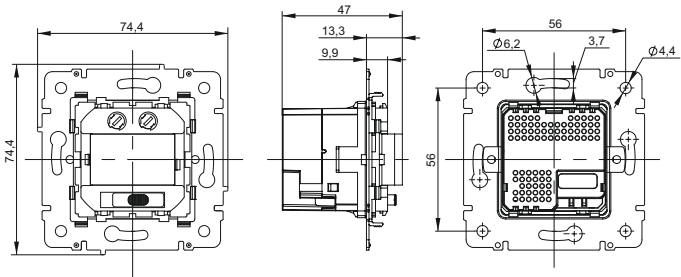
Габаритные и установочные размеры / Figure 1 – Overall and installation dimensions / 1-сურет – Габариттік және орнату өлшемдері / Figura 1 – Dimensiunile generale și de instalare / Şekil 1 – Ümumi və quraşdırma ölçüləri / სკაჲ 1 – ღსუჲასიოჲ Ⴁ სთეოაჲრმას ჯაჲსერე / ნახატი 1 – გაბარიტული და საყენებელი ზომები / 1-сүрөт – Көлөм жана орнотмо өлчөмдөрү / Расми 1 – Андозаи умумий ва насбии / 1-rasm – Umumiy va o'rnatish o'lchamlari
